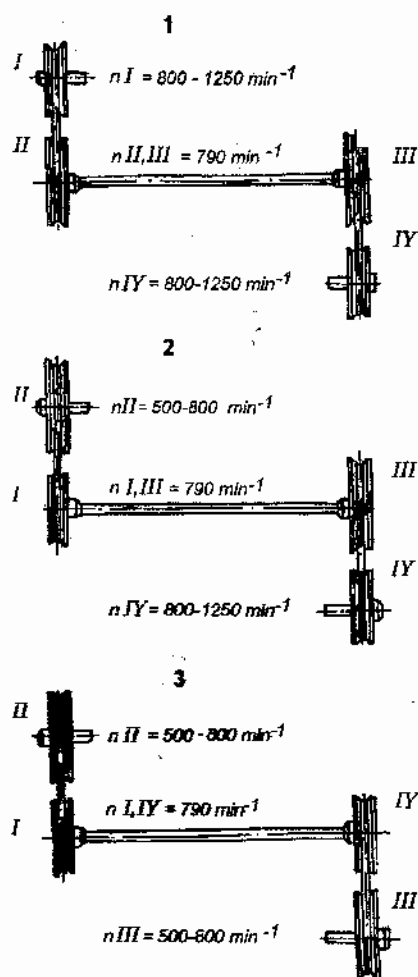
Схема перестановки шкивов барабана и главного контр привода
